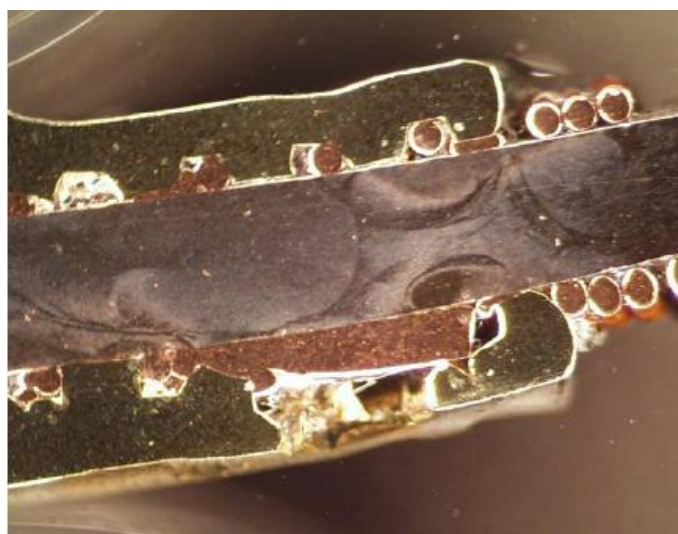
Fotomicrografía de la muestra A1 - L (200 amperes y soldadura actual) (8x) (se observa la fusión del alambre de magneto abajo del pin en la parte central izquierda).
